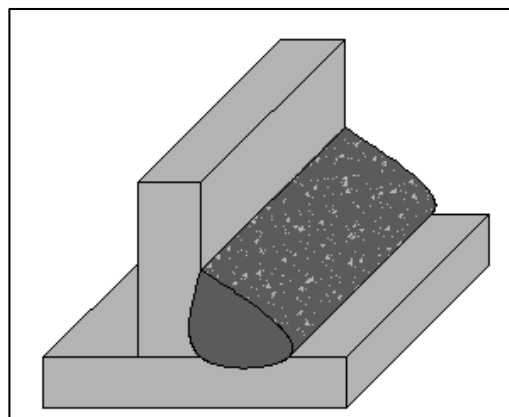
Escoria Atrapada Entre Cordones de Soldadura.
